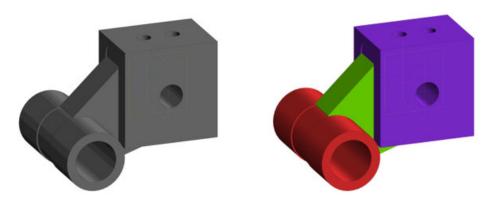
Литая деталь (слева) и сварная конструкция (справа)
